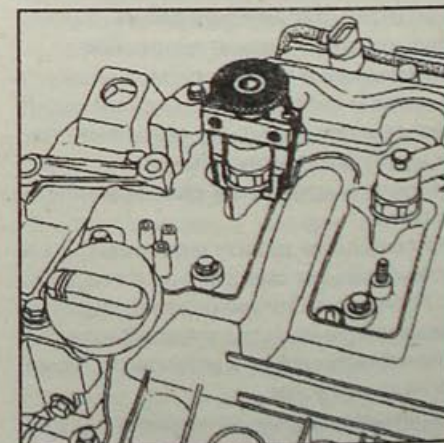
Установка съемника приспособления Mot. 1549 на форсунку
